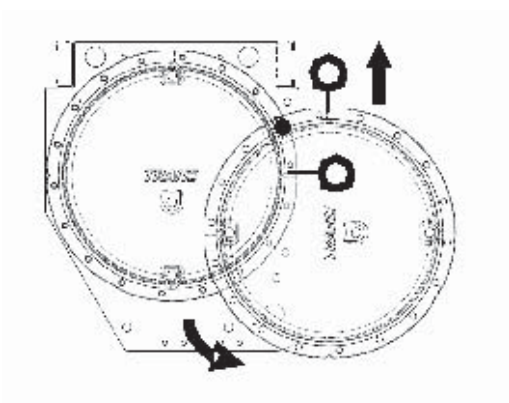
Retrait de la boîte à eau - Pivotement, installation de la chaîne de levage
